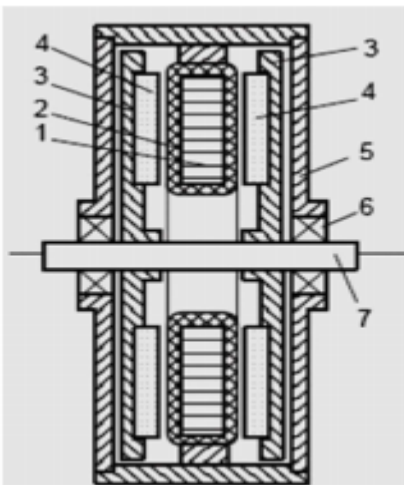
Descriptif de la machine à flux axial 1 stator / 1 rotor.[7]
